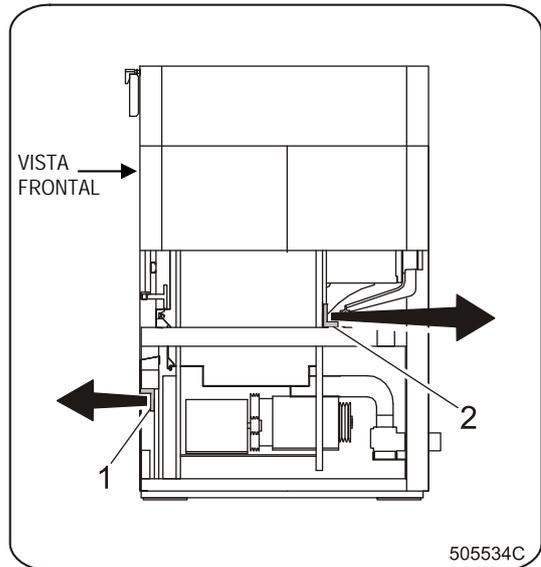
A. Máquinas 33-40-55 kg / 75-90-125 lbs, Soportes de transporte
